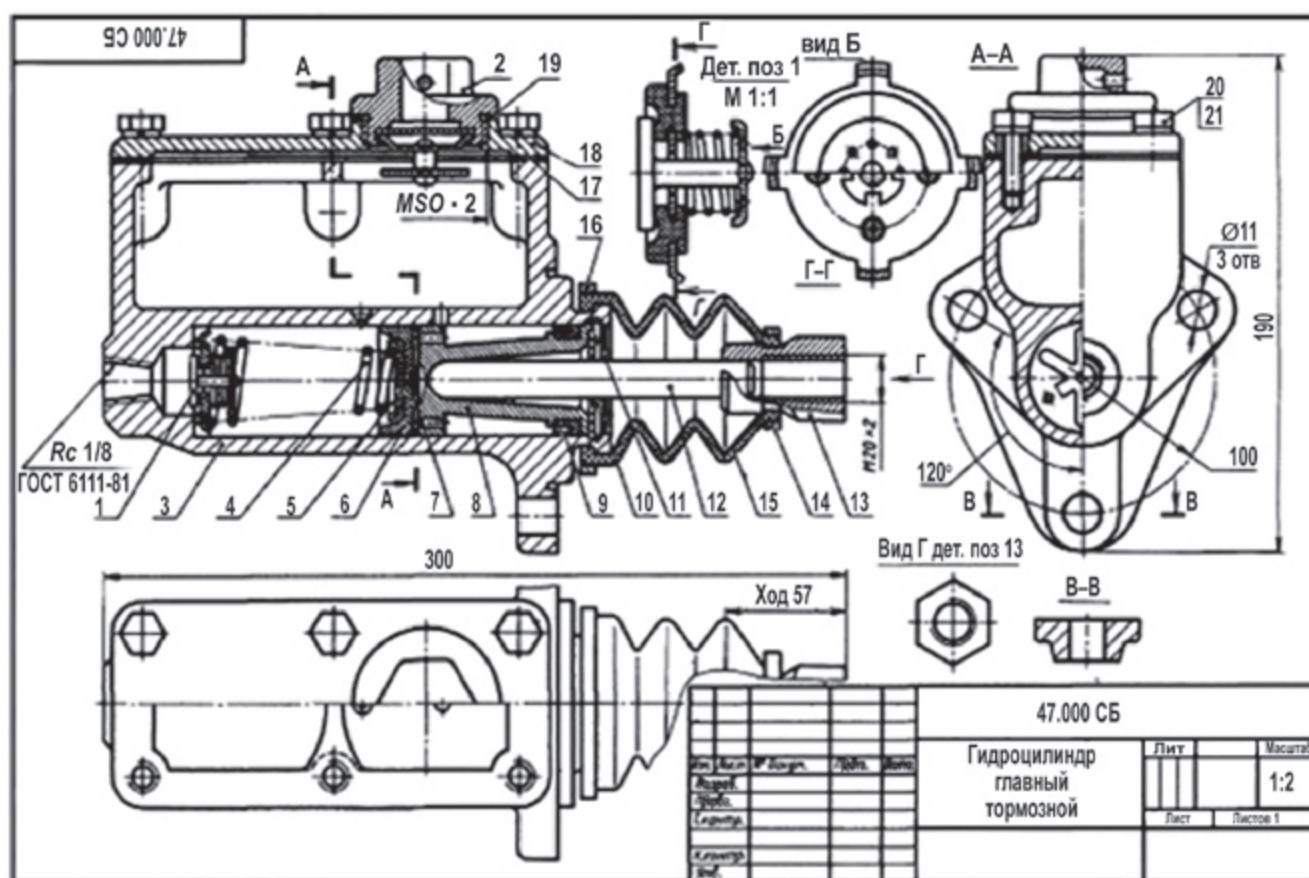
Сборочный чертеж гидроцилиндра главного тормозного. Чертеж № 47.000 СБ
